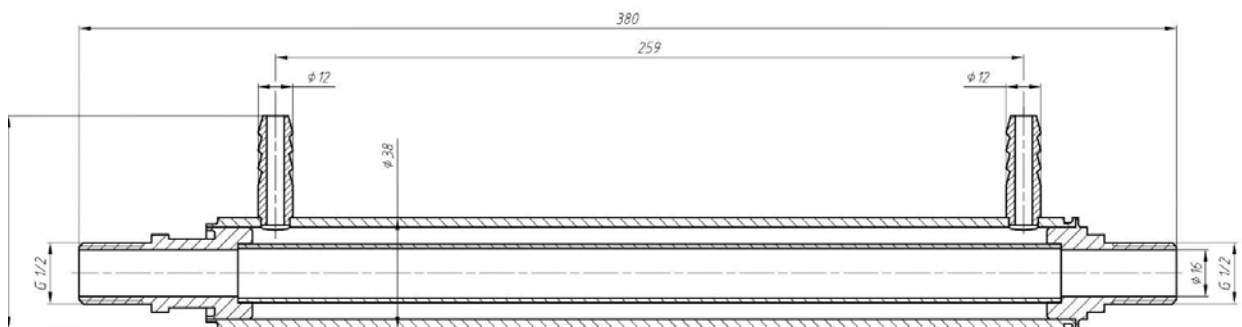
Сборочный чертеж коаксиального резонатора лабораторного реактора СВЧ - пиролиза
